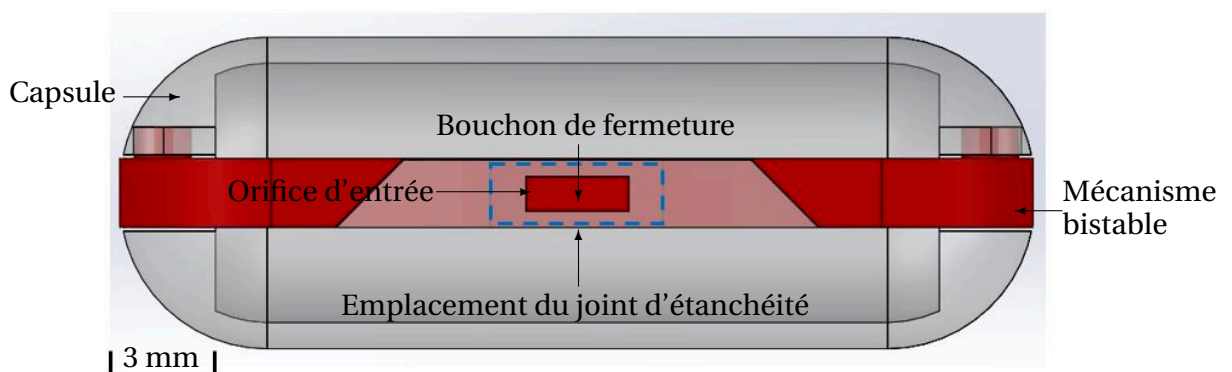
Assemblage de la capsule d'essai d'étanchéité.
